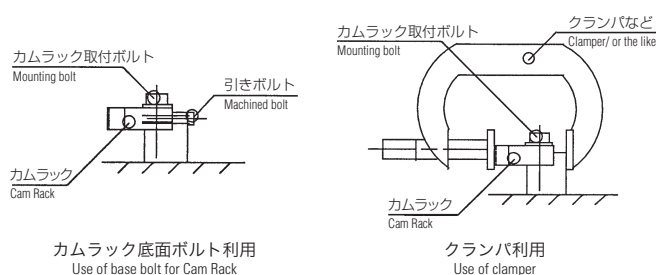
カムラック平行出し方法 Fig. 1 - Setting procedures for parallelism of Cam Rack -
